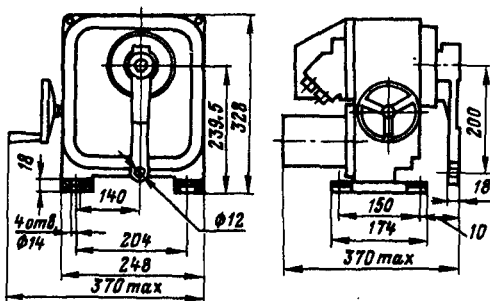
Общий вид, габаритные и установочные размеры МЭО с электродвигателем ДАУ
